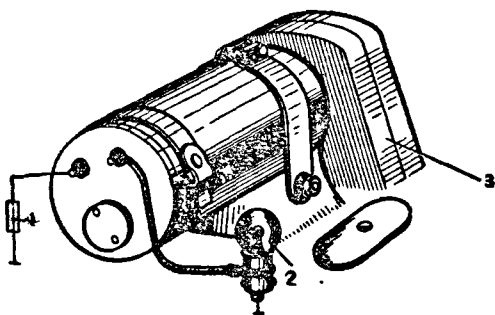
Проверка генератора на двигателе: 1 — предохранитель; 2 — контрольная лампа; 3 — двигатель
